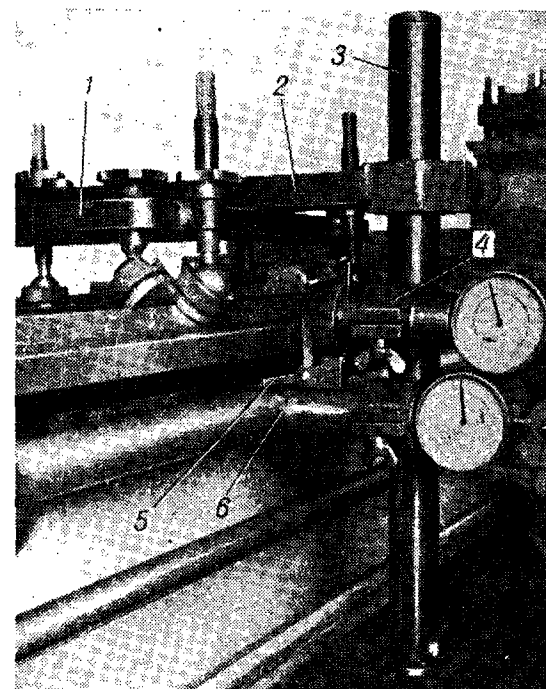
Приспособление для проверки параллельности осей ходовых винтов и валов
